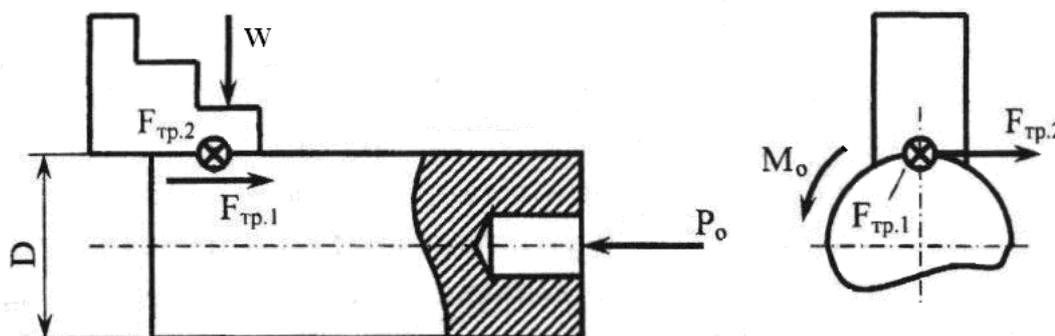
Схема к определению силы закрепления заготовки при сверлении отверстия на токарном станке
